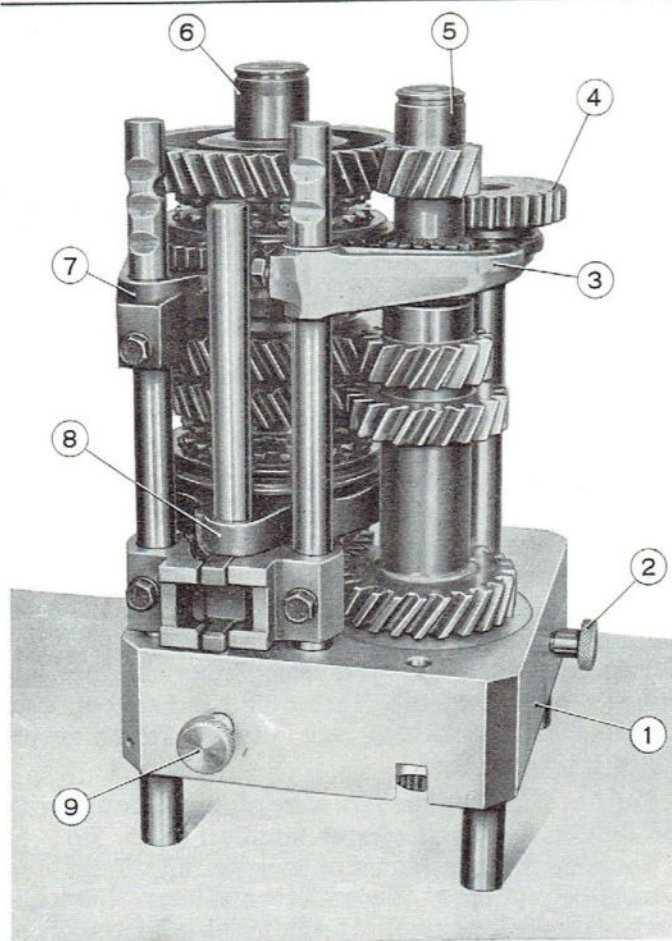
Vorbereitende Montage des Getriebes auf dem Werkzeug A. 70105.
